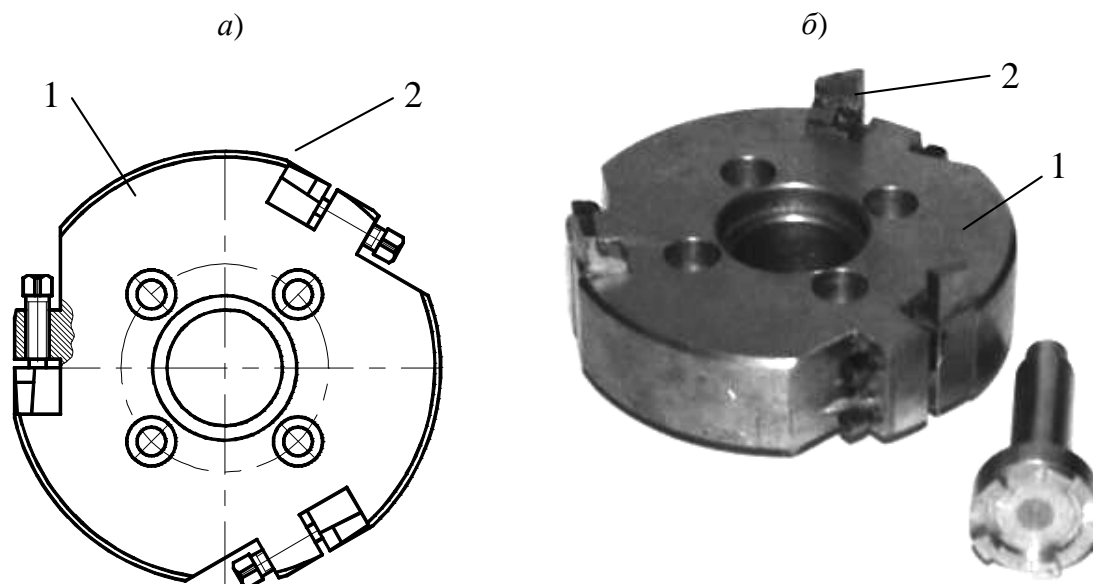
Инструмент к станку модели ВС-50 для обработки торцового зубчатого контура: *a* – конструкция инструмента; *б* – общий вид инструмента с обработанной деталью
